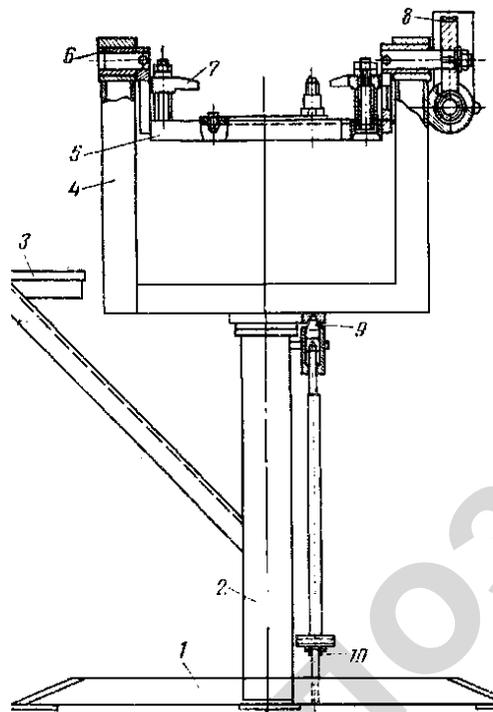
Схема станда для разборки и сборки компрессора:
